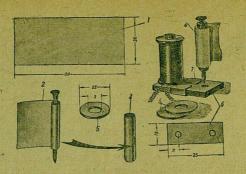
Электромагнит пишущего реле: I — полоска жести, которой обертывается гвоздь, 2 — обертывание гвоздя, 3 — готовая спаянная обертка, 4 — полоска бумажной ленты, 5 — щеки катушек, 6 — жестяная пластинка ярма, 7 — обойма, скрепляющая набор пластинок ярма.
